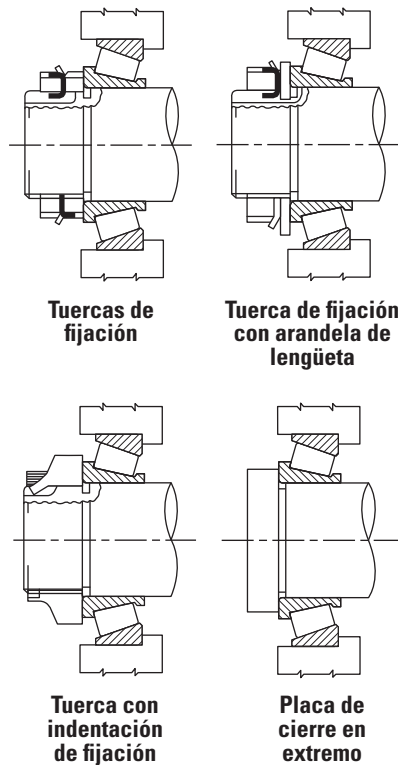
Dispositivo de regulación de rodamiento, montaje indirecto.
